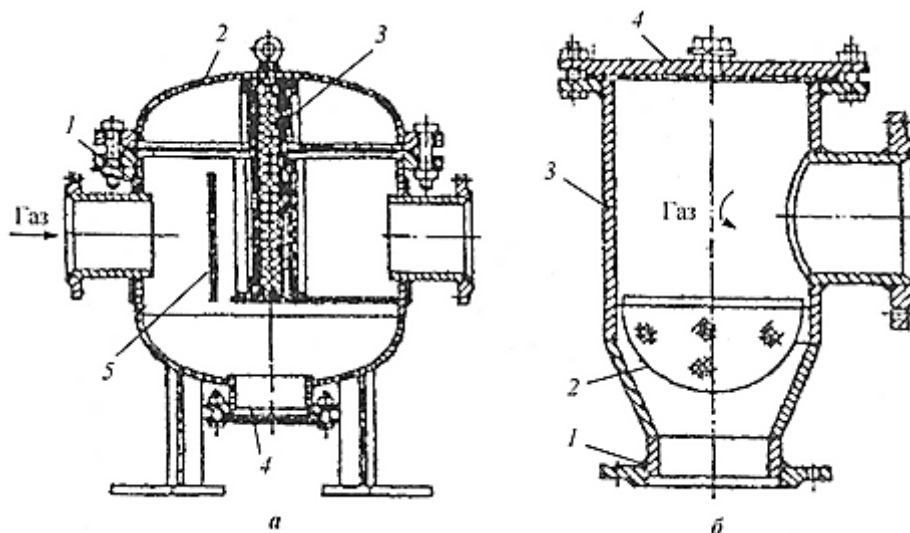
Фильтры сварные: *а* – фильтр стальной сварной: 1 – сварной корпус, 2 – верхняя крышка, 3 – кассета, 4 – люк для чистки, 5 – отбойный лист; *б* – фильтр-ревизия: 1 – входной патрубок, 2 – сетка, 3 – корпус, 4 – крышка
